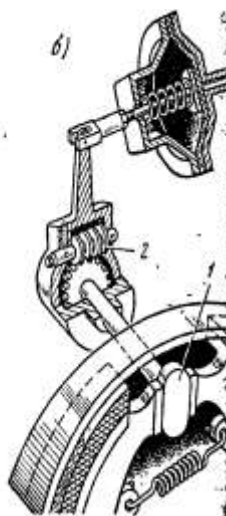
Регулировка тормозного механизма с пневмоприводом: 1 - разжимной кулачок, 2 - червяк регулировочный.
